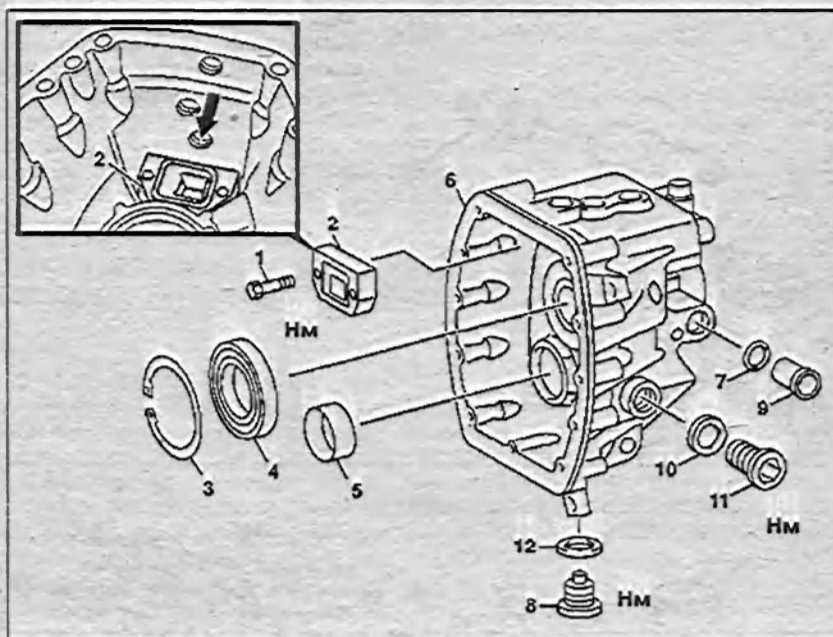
а. Задняя часть корпуса коробки передач 711.603:
